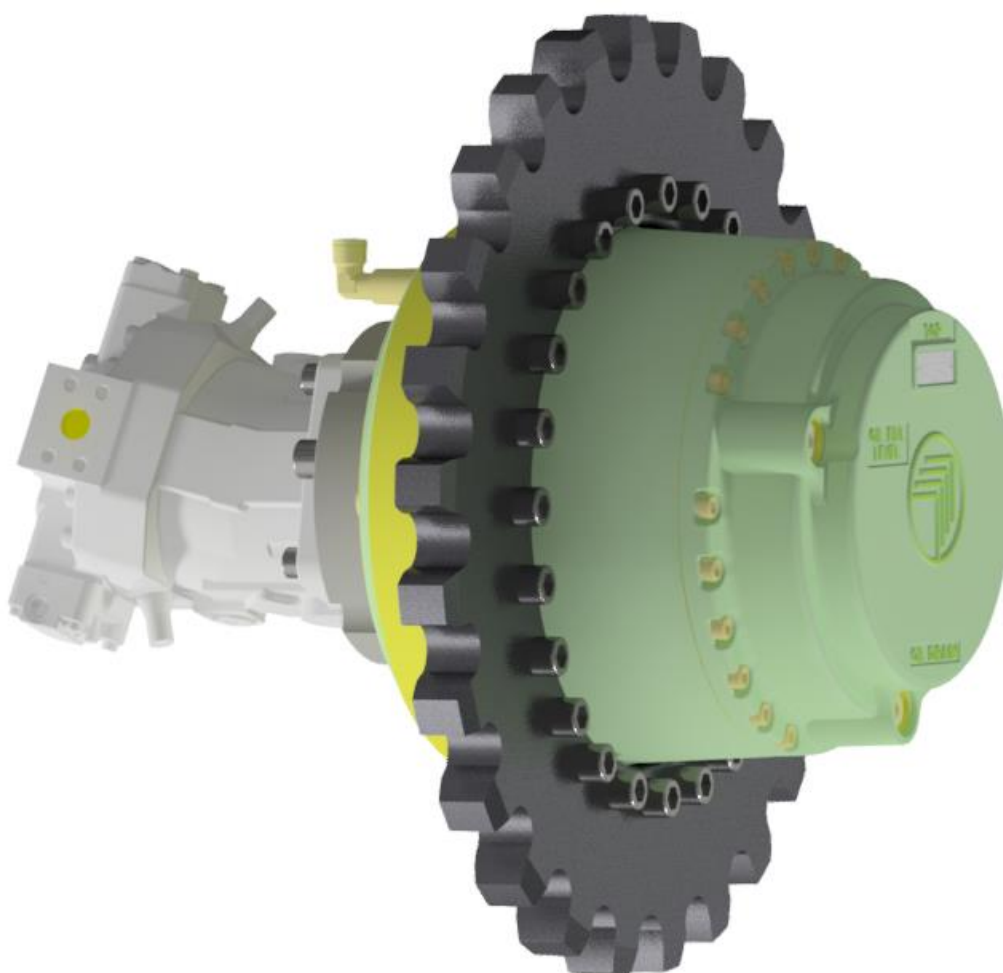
Planetová převodovka Bonfiglioli 711 C3 B [27]
